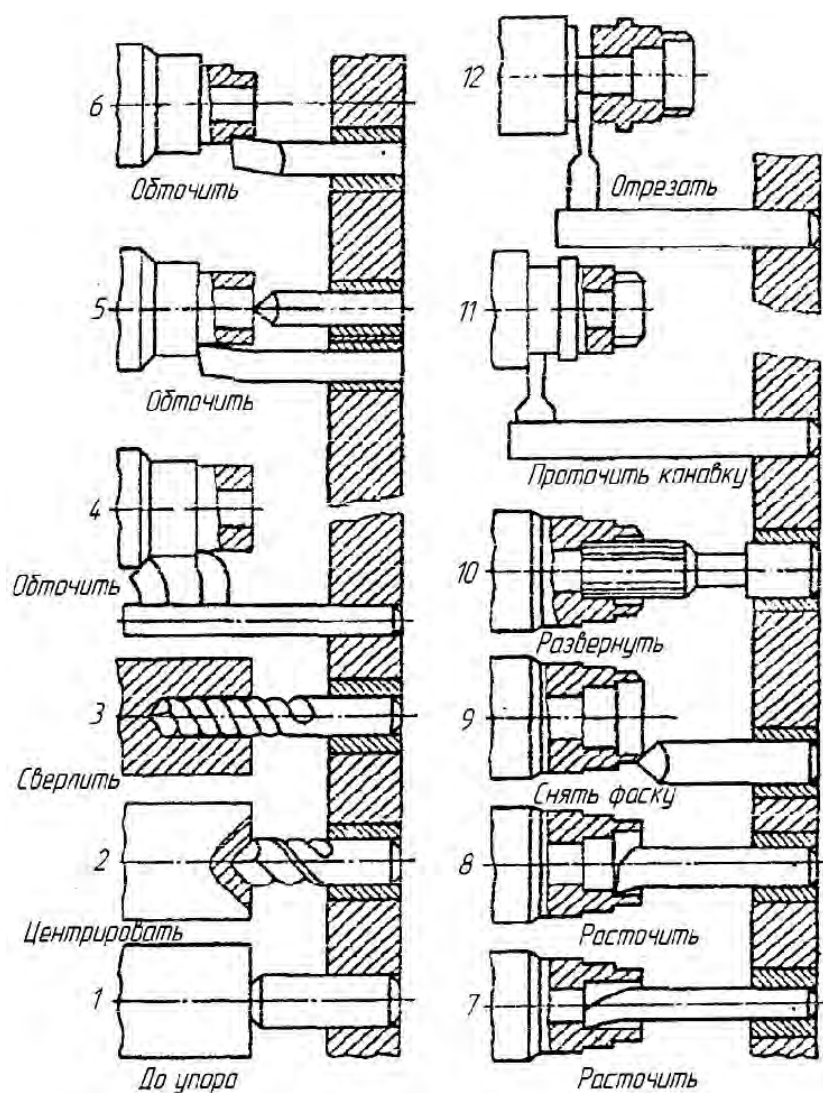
План обработки оправы на токарно-револьверном станке
